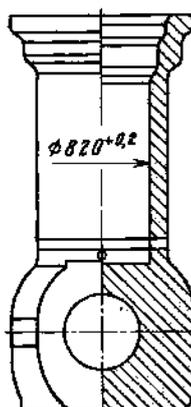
Сварно-кованый подъемный цилиндр шагающего экскаватора ЭШ-15/90А
